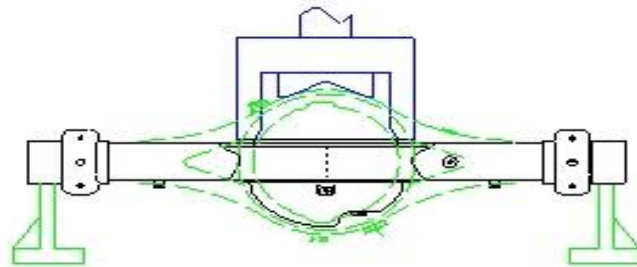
Proses *bracket install welding assy human* di Stasiun Kerja M-16.2
